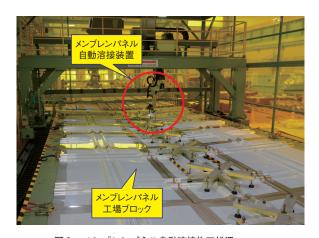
メンブレンパネル自動溶接施工状況 Fig. 8 Automated welding of membrane panels
